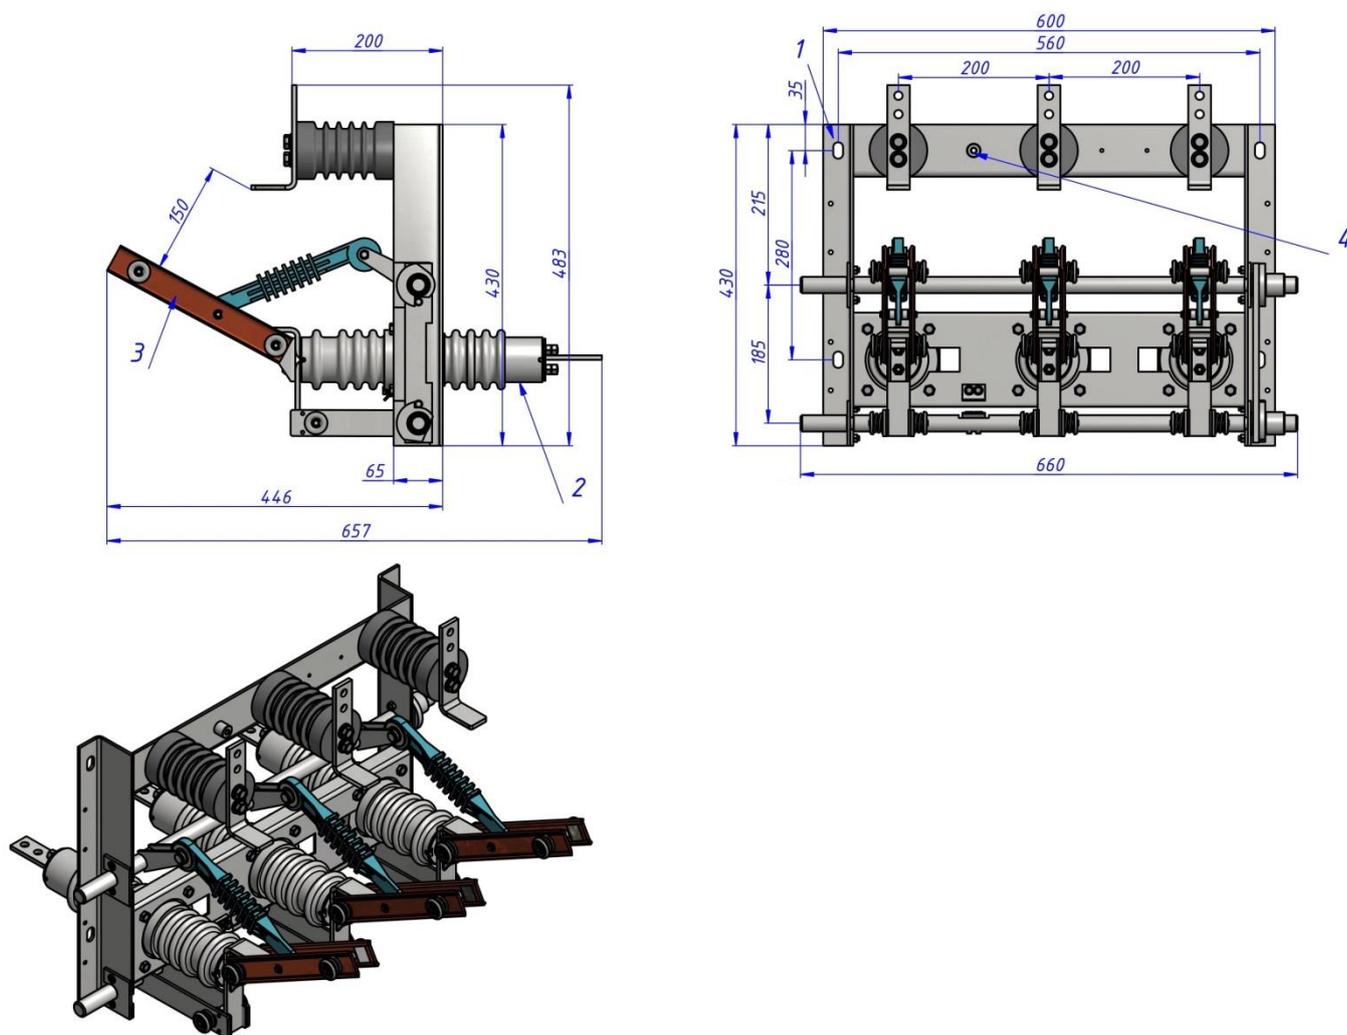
Габаритно-установочные размеры и устройство разъединителя РВФЗ
